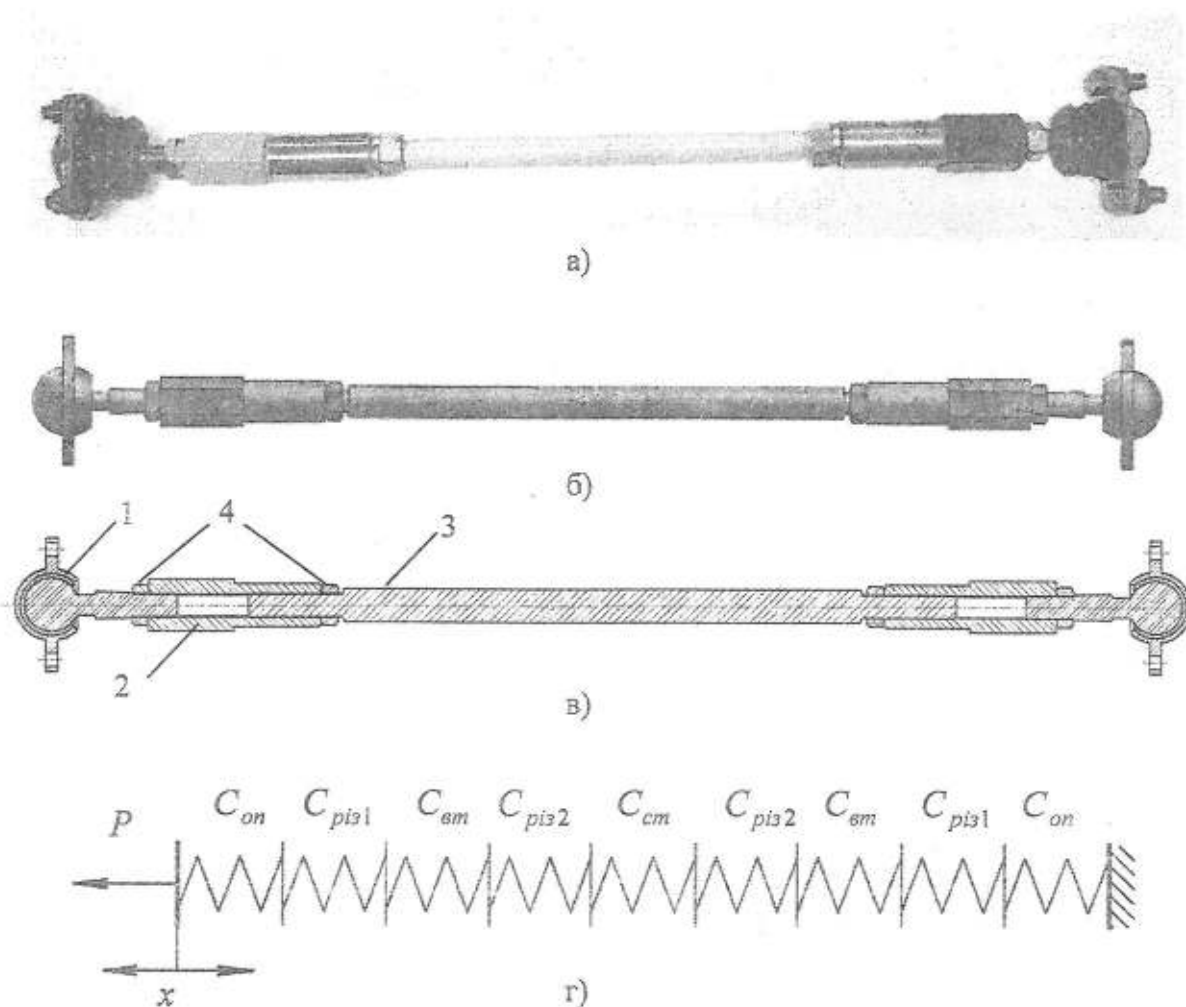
Штанга постійної довжини: а) – виготовлений зразок; б) і в) – 3D і 2D CAD модель конструкції штанги, відповідно; г) – розрахункова схема. 1 – шарова опора; 2 – втулка; 3 – стержень; 4 – контргайка
